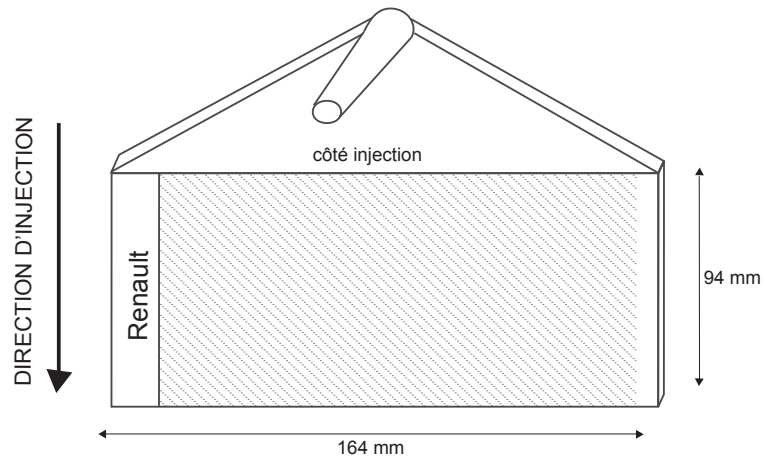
Dimensions et géométrie de la plaque injectée.
